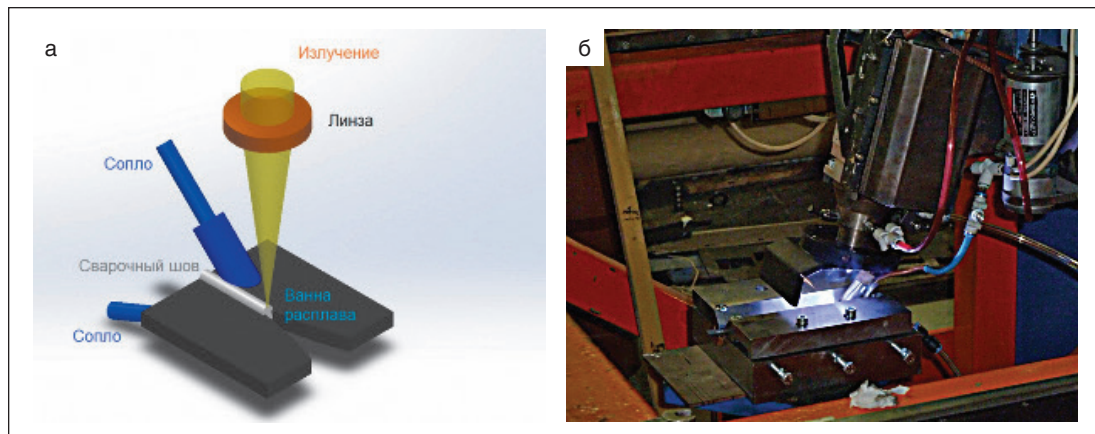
Технологическая схема лазерной сварки (а) и лабораторный стенд (б)
